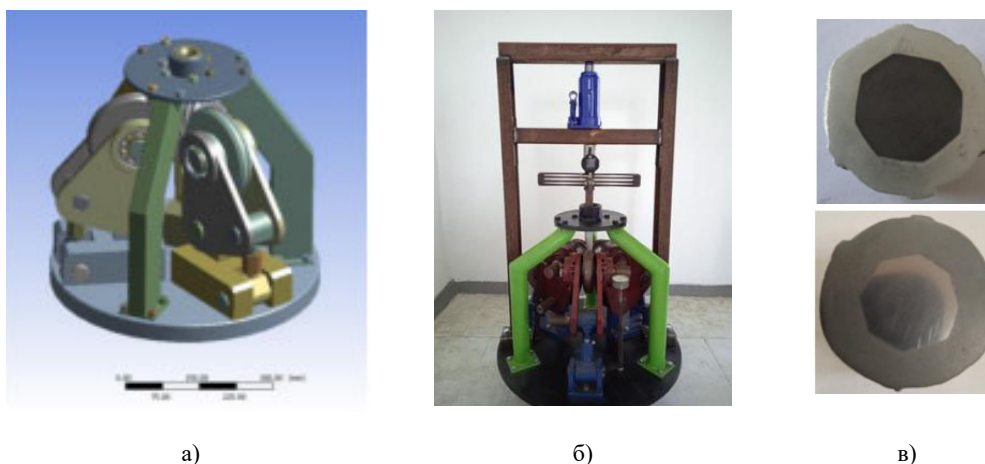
Трироликова волока для зовнішнього обтиснення циліндричної заготовки на профільній оправці неприводними роликами: а – CAD-модель; б – загальний вигляд експериментальної установки; в – отримані трубчасті деталі з полігональним профілем каналу [9]
